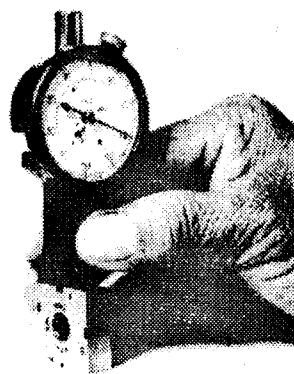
Непрерывный циферблатный калибр высоты, приложенный к установочному эталону
